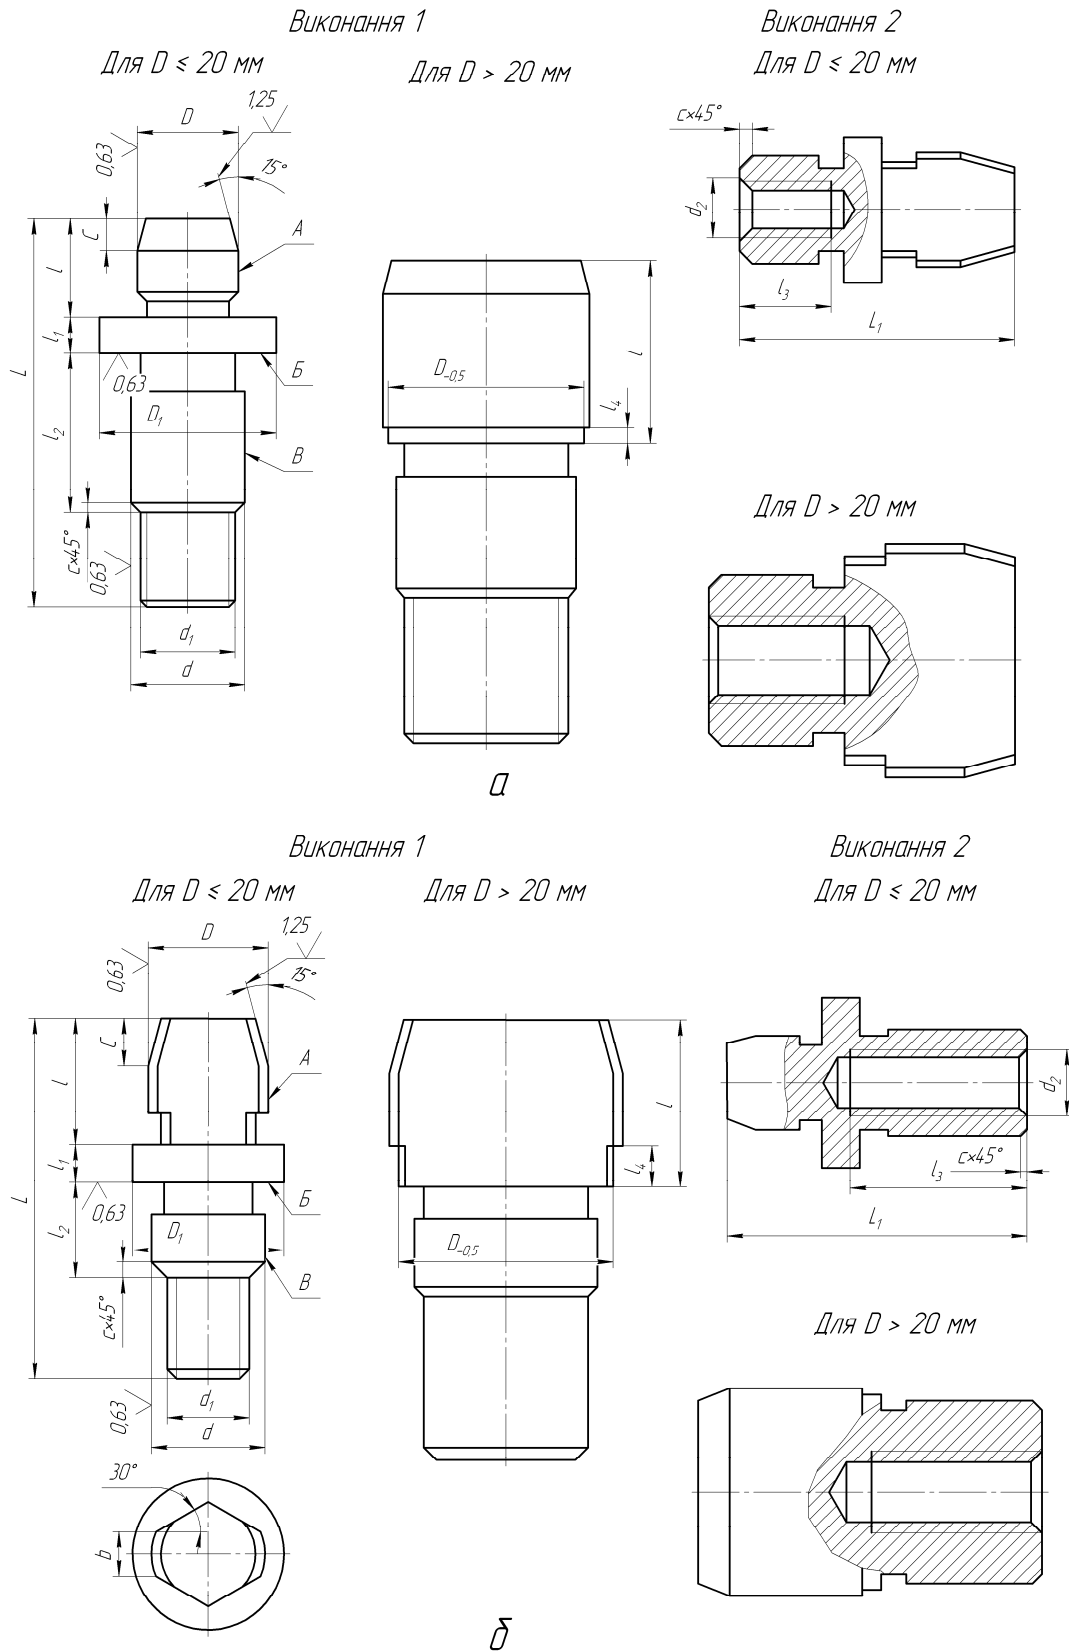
Схеми встановлення корпусних деталей за допомогою двох отворів: а – циліндричні (ГОСТ 12211-66); б – зрізані (ГОСТ 12212-66)
